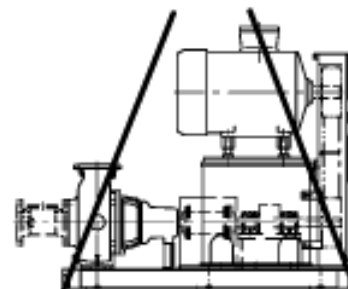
Транспортировка насосного агрегата в сборе (тип установки 3H с редуктором)
